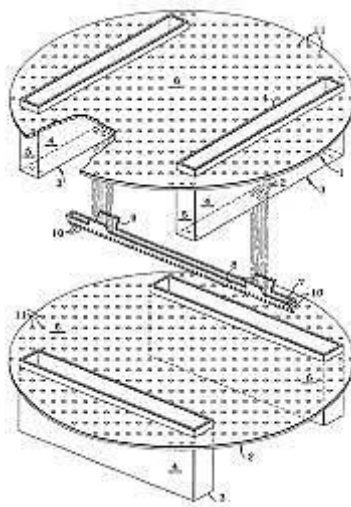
Plato tamizado de la columna DC-302.
